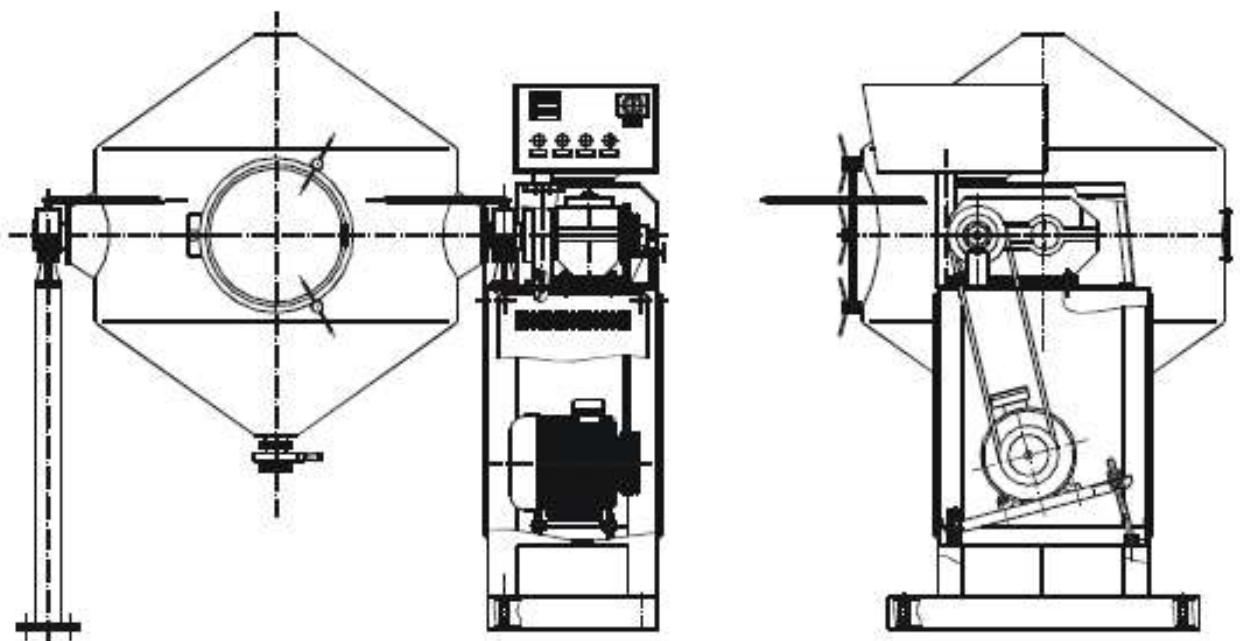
Маслоутворювач типу РЗ-ОБЗ.
